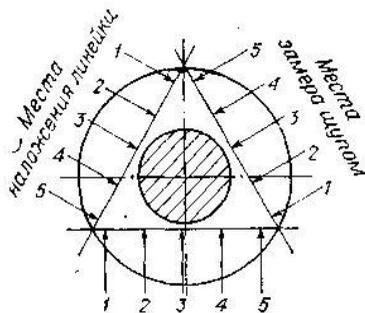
Схема проверки поверхности упорного диска контрольной линейкой и щупом.
